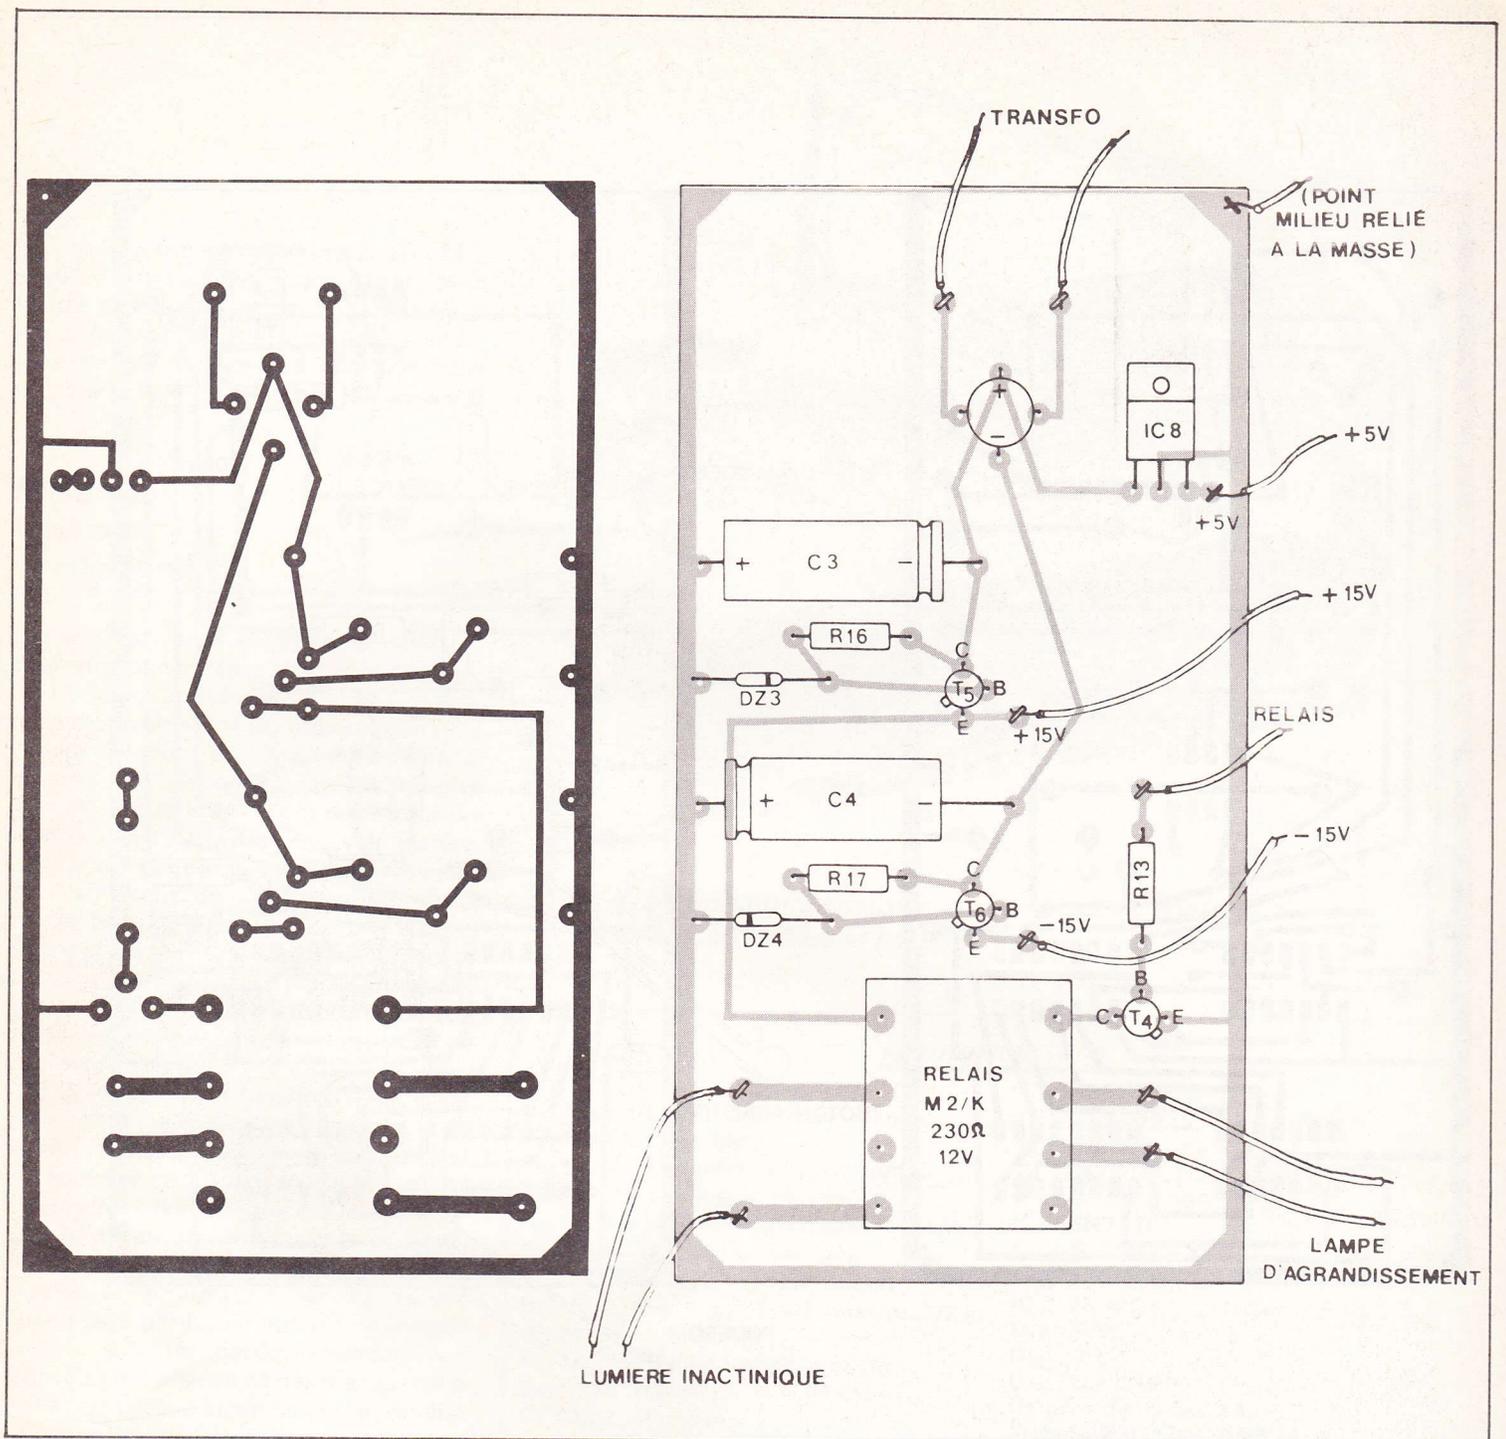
et 6b. – Tracé et implantation, échelle 1, de la section alimentation. Le relais trouve également sa place sur ce circuit mais attention au brochage de celui que vous utiliserez.
